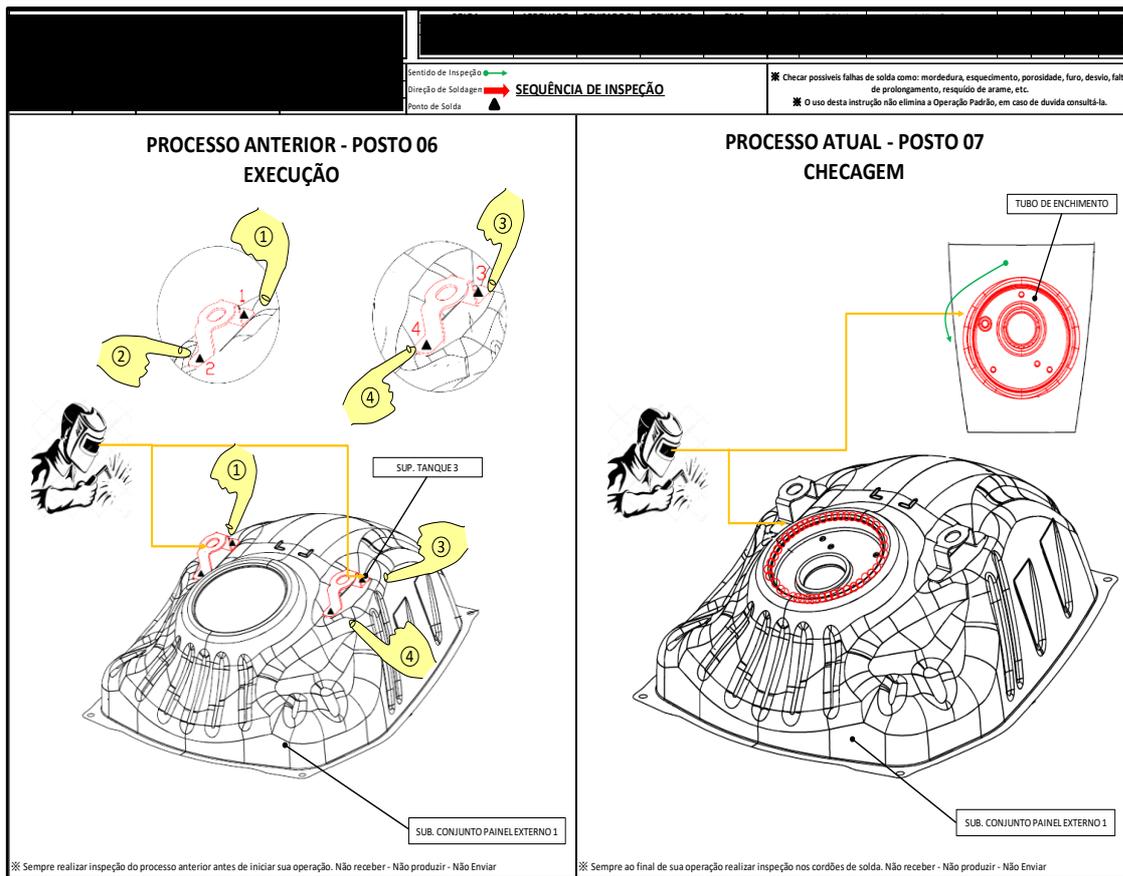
Instrução de pontos de atenção da soldadura do tanque
